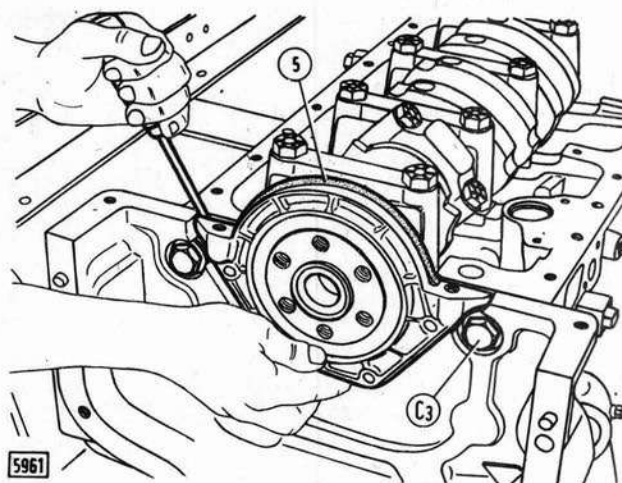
Dépose du joint arrière du vilebrequin.
